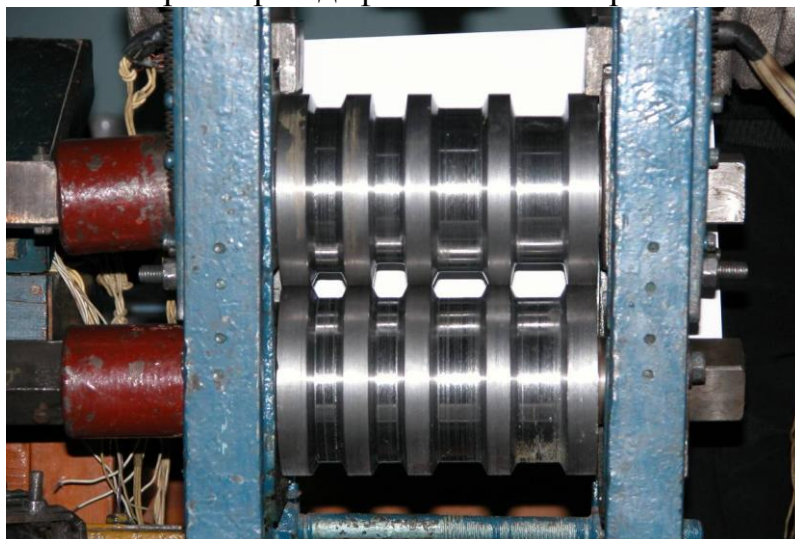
Внешний вид клетки лабораторного стана: моделируемое сечение непрерывнолитой заготовки – 125x125 мм, масштаб моделирования 1:5
